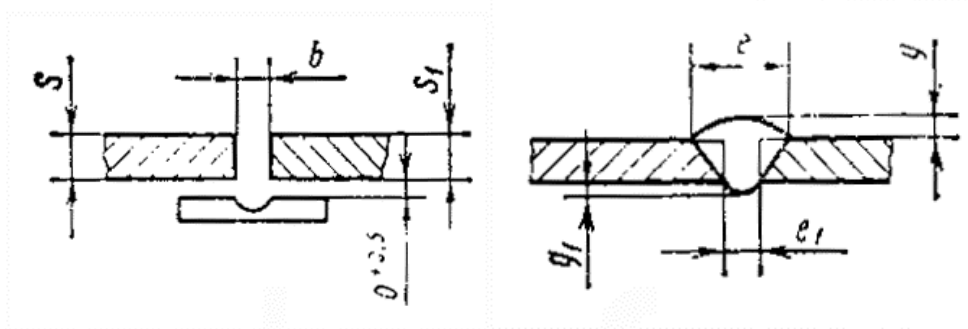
по ГОСТ 14771-76, сварной шов №2
